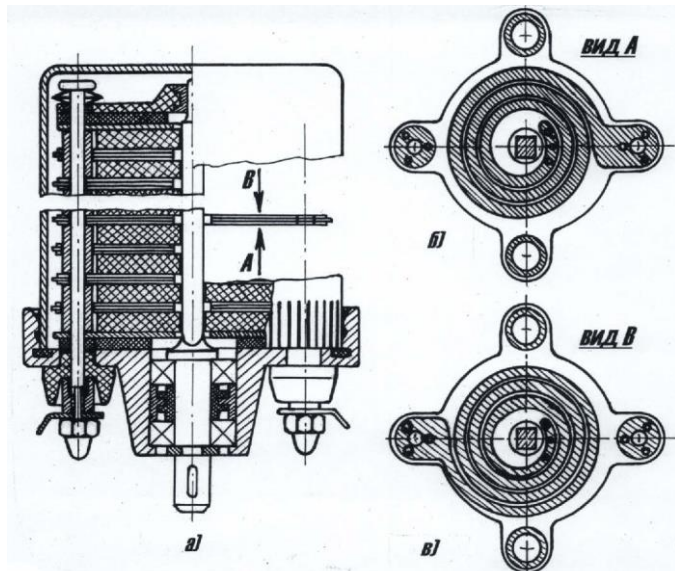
Галетный электродвигатель: поперечный разрез (а) и виды сторон галет с печатными обмотками (б, в).
